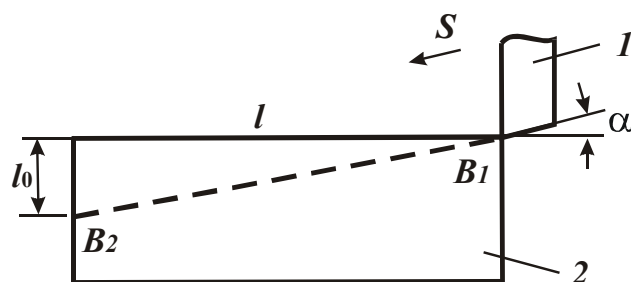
Розрахункова схема кута α : 1 – різець; 2 – деталь.
